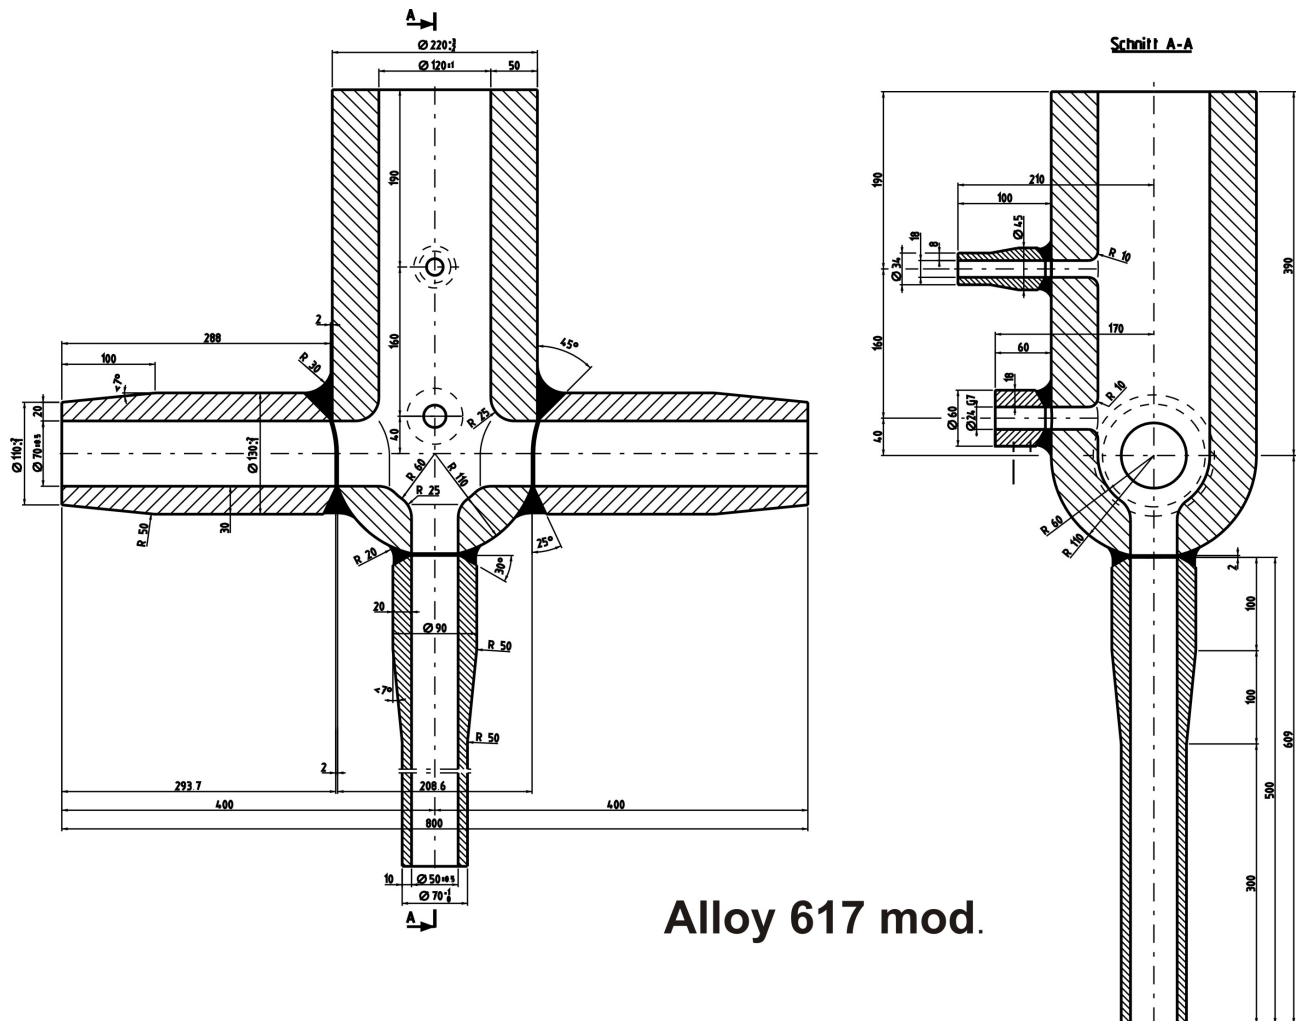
Ausschnitt der Technischen Zeichnung von BPT des Halbkugelformstücks aus Alloy 617 mod.
